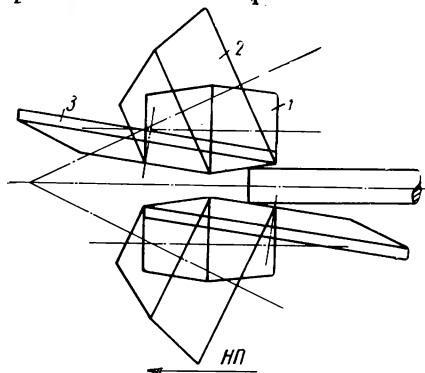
Схема расположения валков прошивных станов с бочкообразными (1), грибовидными (2) и дисковыми (3) валками
